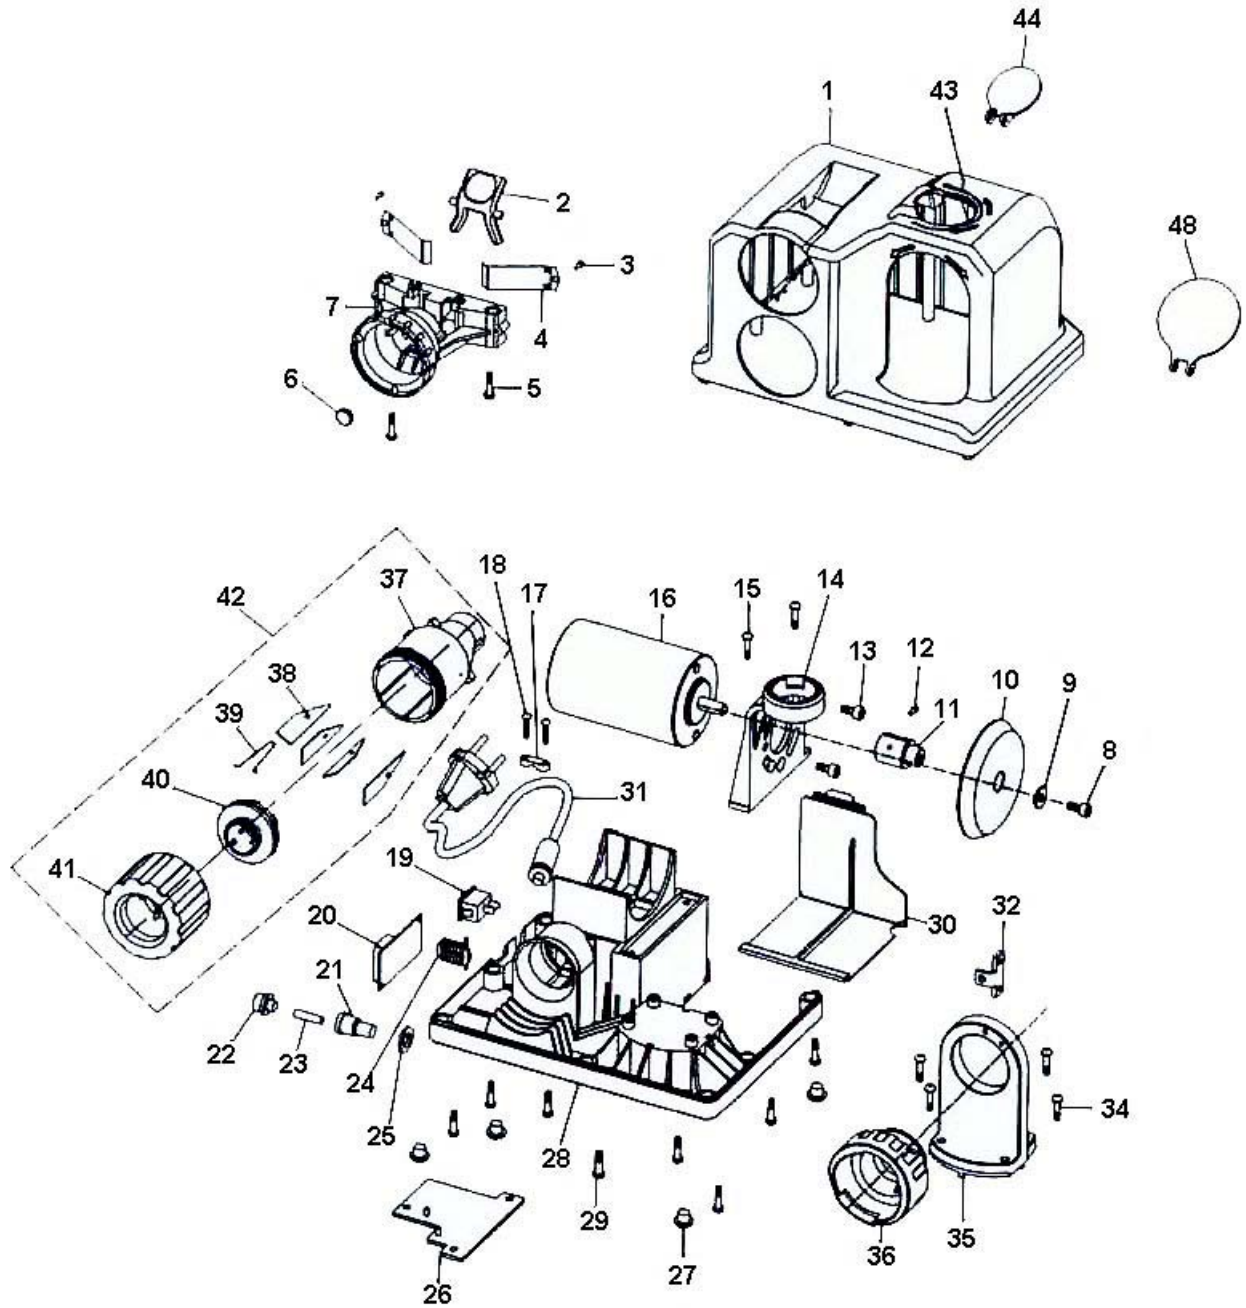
Ersatzteilzeichnung - Drawing spare parts GQ-D13
